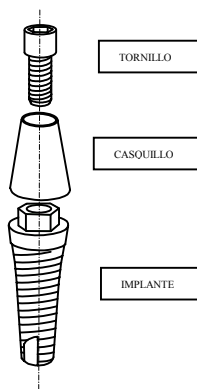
Esquema de la disposición de elementos que componen un implante dental.
